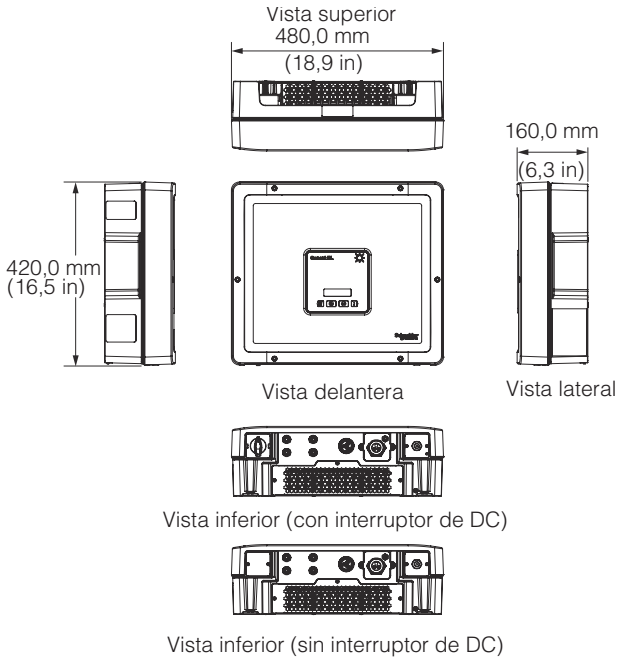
Vistas y dimensiones de Conext RL 3000 E-S/3000 E
